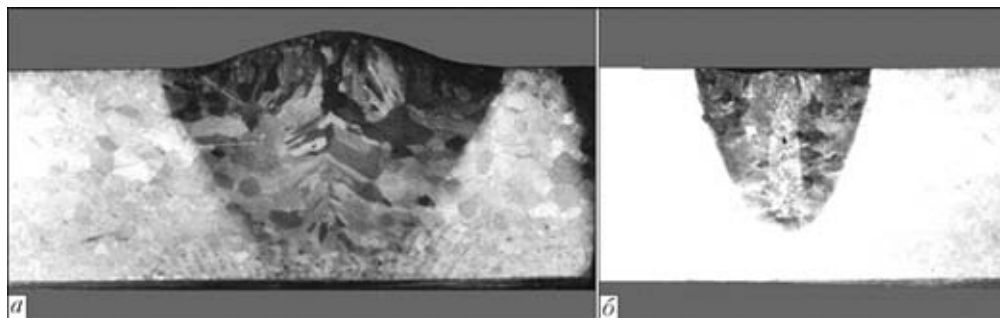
Поперечный макрошлиф наплавки на титановом сплаве Т110 толщиной 13 мм: а – лазерно-дуговая сварка, б – лазерная сварка
